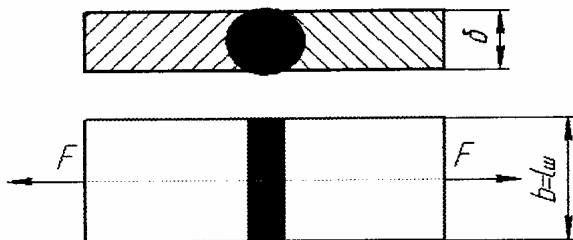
Расчет стыкового сварного соединения
